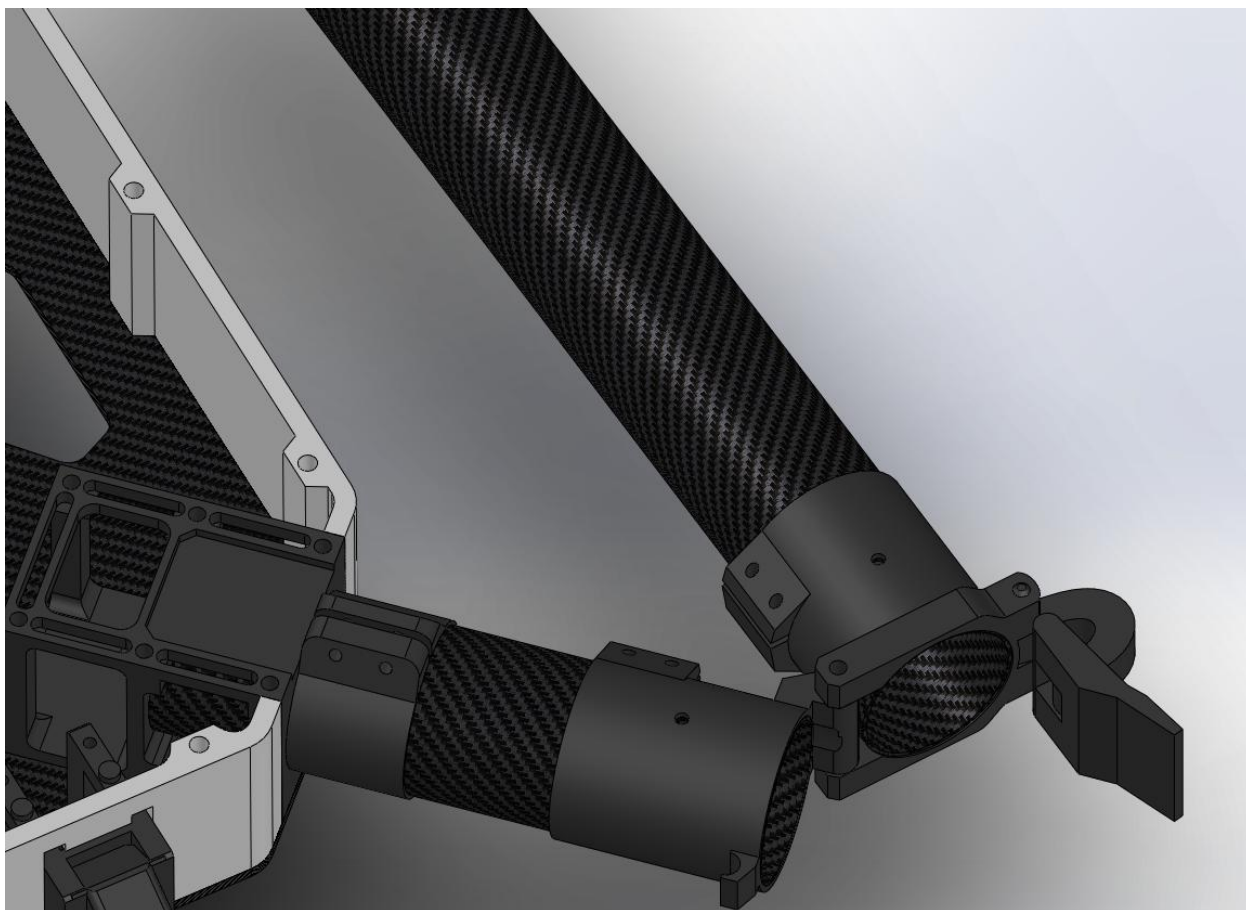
Шарнирный механизм складывания лучей БВС
